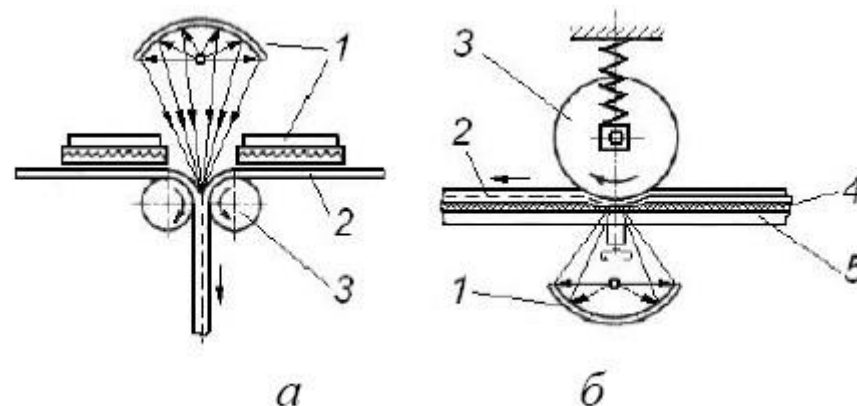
Сварка пленок световым лучом прямым (а) и косвенным (б) нагревом: 1 – источники света; 2 – свариваемый материал; 3 – прижимные ролики; 4 – резиновая прокладка; 5– кварцевый диск
